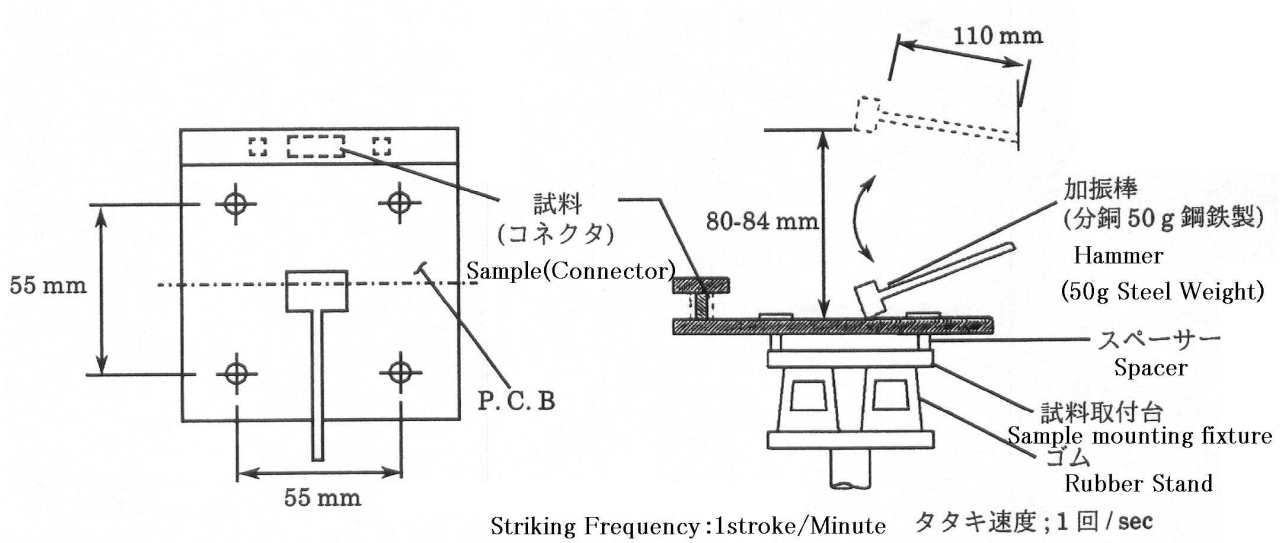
微加振動試験方法 / Method of Hammering Shock Test
